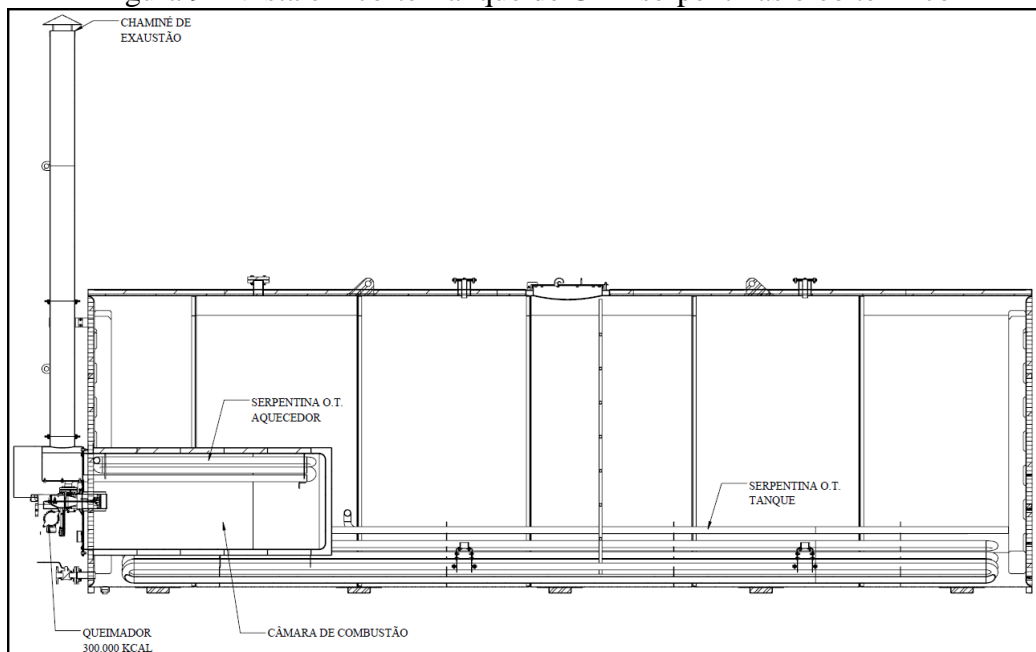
Vista explodida Tanque de CAP serpentinas óleo térmico
